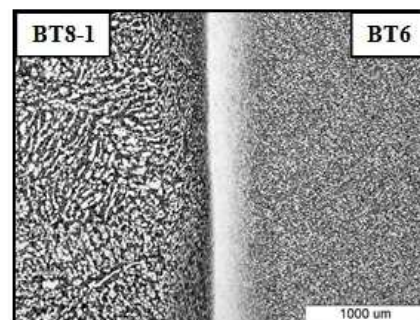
Зона сварного шва сплавов ВТ8-1 и ВТ6, подвергнутых линейной сварке трением с коэффициентом деформации $\lambda = 3$
